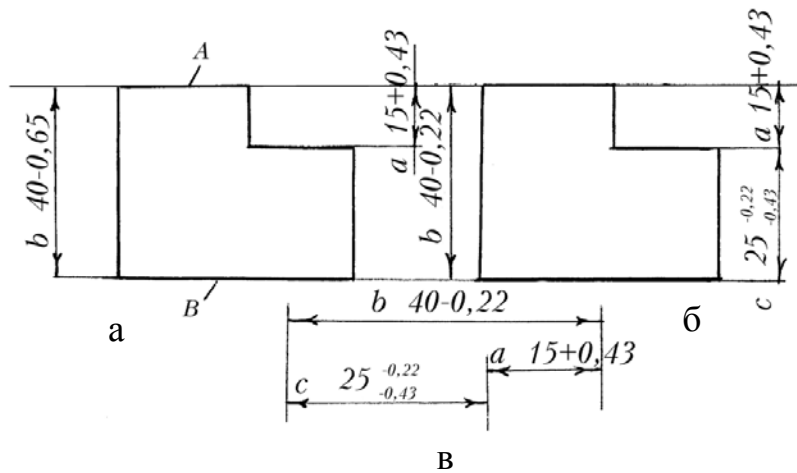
Креслення деталі (а) і ескіз обробки (б).
